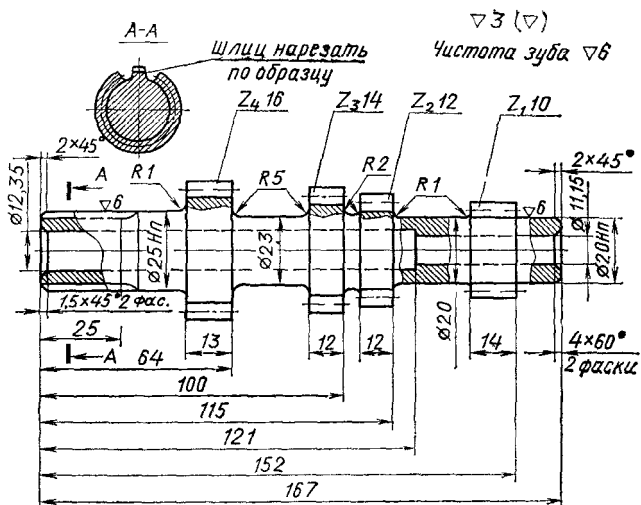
Первичный вал к спортивной коробке передач. Данные для изготовления шестерен первичного вала:
